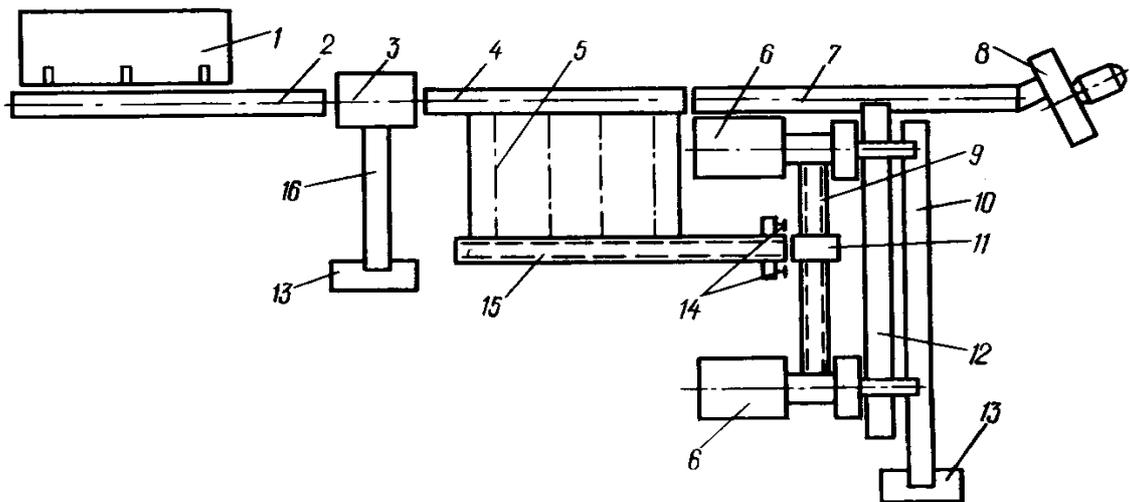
Технологическая схема линии для выработки балансов и щепы из низкокачественной древесины: 1 – буферный магазин; 2 – приемный транспортер окорочного станка; 3 – окорочный станок; 4 – лесотранспортер; 5 – приемная площадка окоренных бревен; 6 – станок для выколки гнили; 7 – продольный лесотранспортер; 8 – рубительная машина; 9 – приемная площадка станка для выколки гнили; 10 – транспортер уборки отходов; 11 – приемный стол разделочной установки; 12 – цепной, или ленточный, лесотранспортер; 13 – приемные люки; 14 – разделочная установка; 15 – продольный транспортер разделочной установки; 16 – транспортер для удаления коры от окорочного станка
